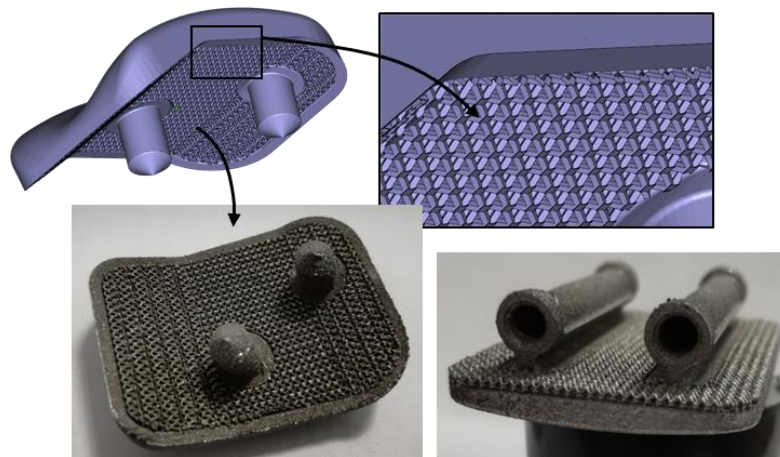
Dal CAD al componente fabbricato tramite SLM: la componente talare.
